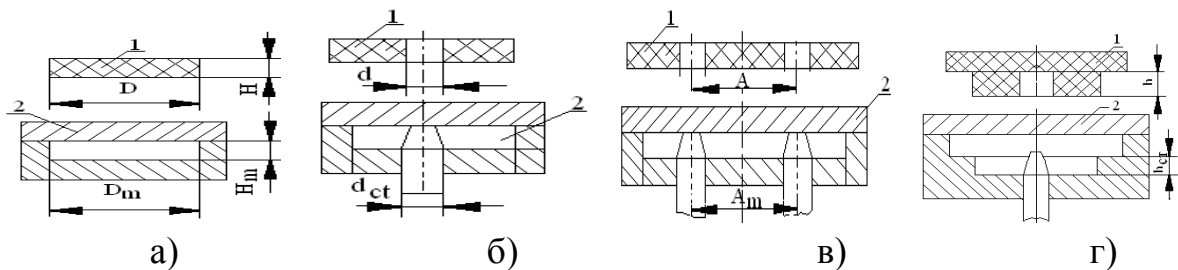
Оформляючі деталі ливарної форми:
